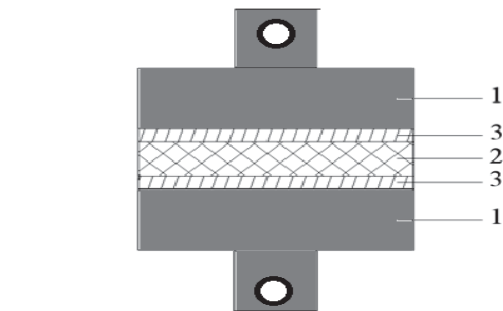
Схема образца для испытания по ГОСТ 209-75 – определение прочности связи резины с металлом при отрыве: 1 – металлические диски; 2 – резиновый массив; 3 – клеевая пленка
